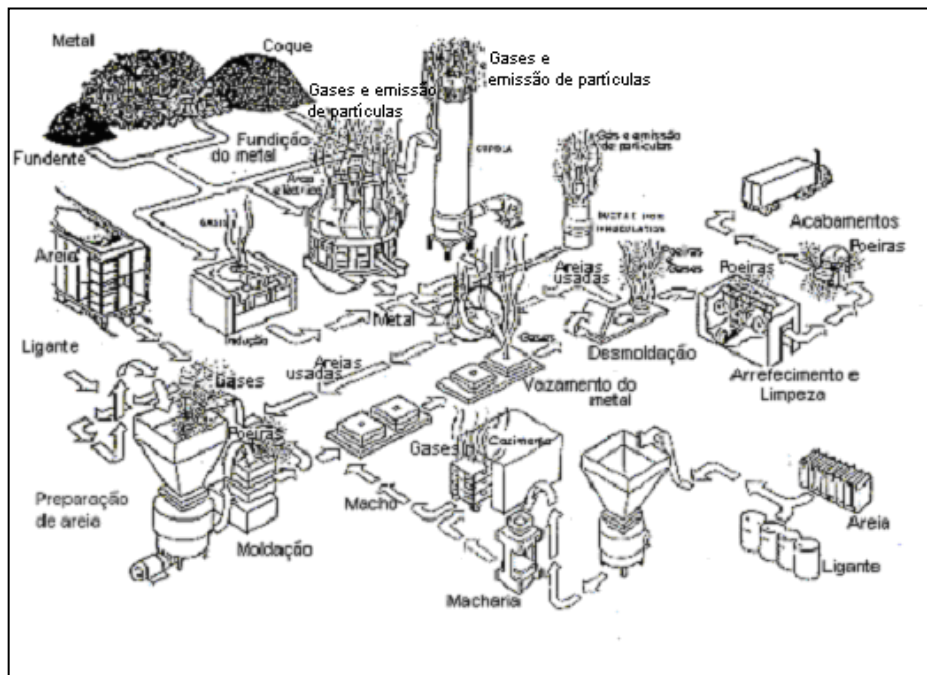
Diferentes etapas do processo de fundição com moldagem em areia (Adaptado de Moreira, 2004)
